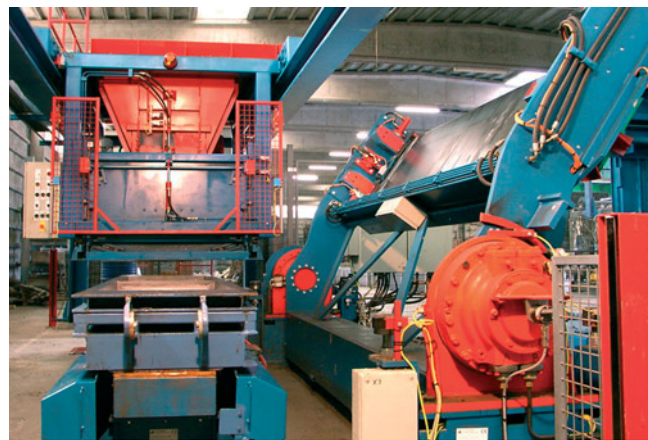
Ensemble de moulage-démoulage avec bridage du moule sur poutre vibrante
